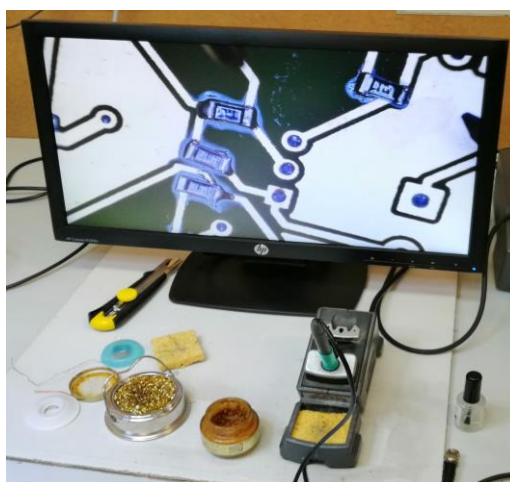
Comprobación de la soldadura de los componentes SMD
